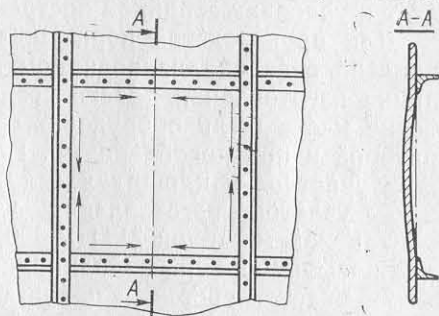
Схема деформации смещения деталей при контактной сварке.
